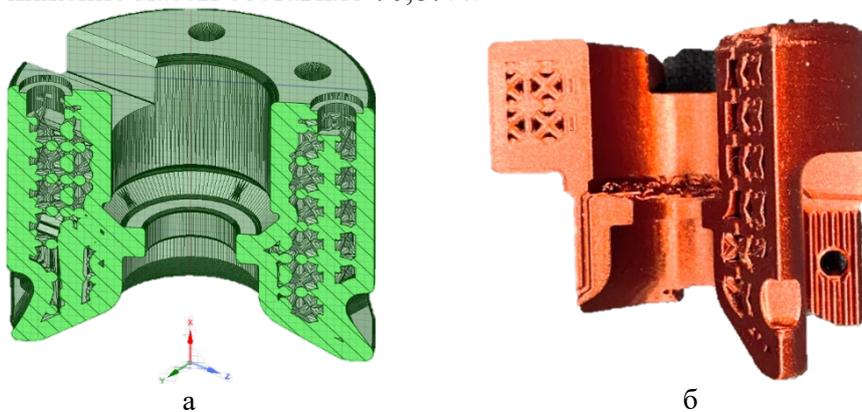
Оптимизированный корпус торцевой фрезы в разрезе
